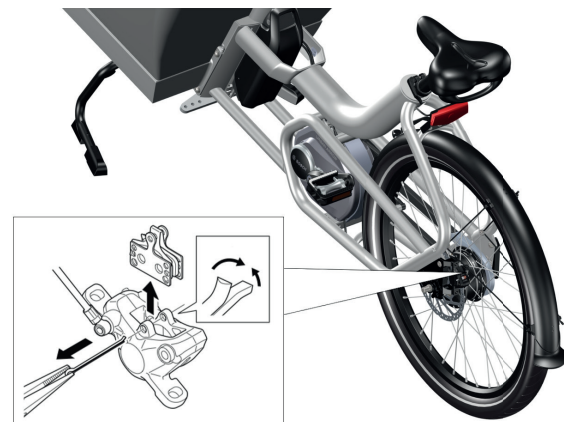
Entfernen der Bremsbeläge, um sie auf Verschleiß zu prüfen
